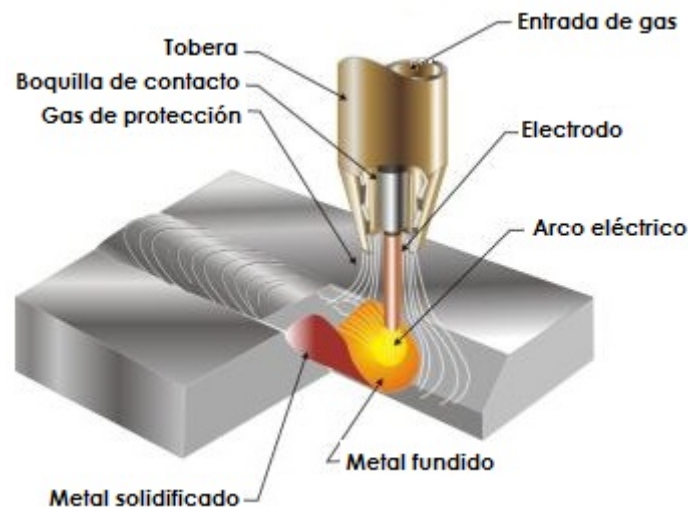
Principio del proceso de la soldadura (GMAW). [17]
